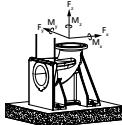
Допустимые присоединительные нагрузки на фланцы
